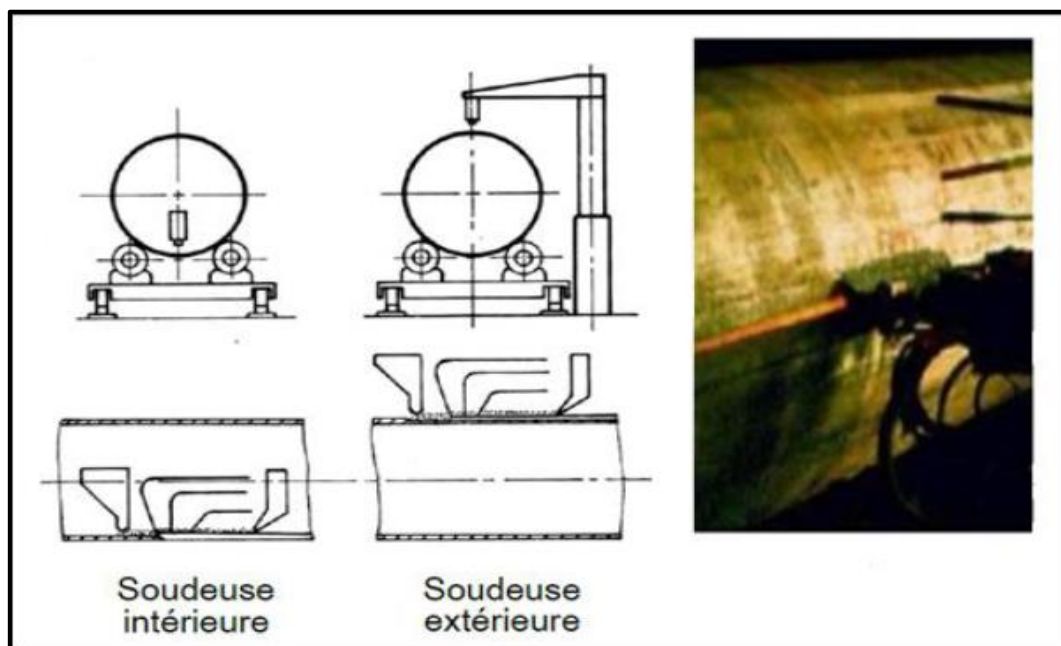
Soudage des tubes par le procédé « UOE » [6].
